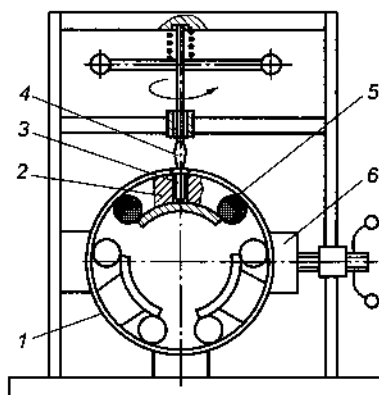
Приспособление для зажима корпуса стартера: 1 — корпус стартера; 2 — полюсный наконечник; 3 — винт крепления полюсного наконечника; 4 — отвертка; 5 — обмотка возбуждения; 6 — зажим
